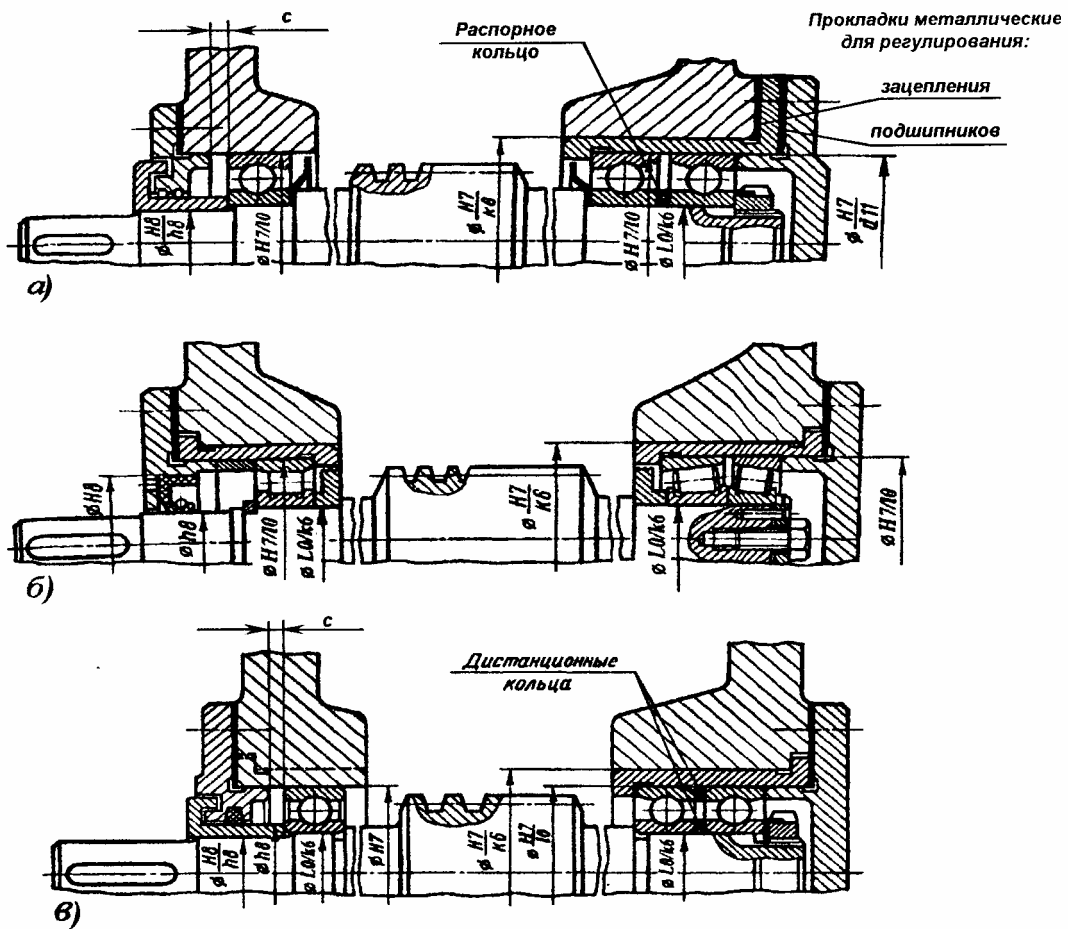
Конструкции фиксирующих опор с двумя радиально-упорными подшипниками
